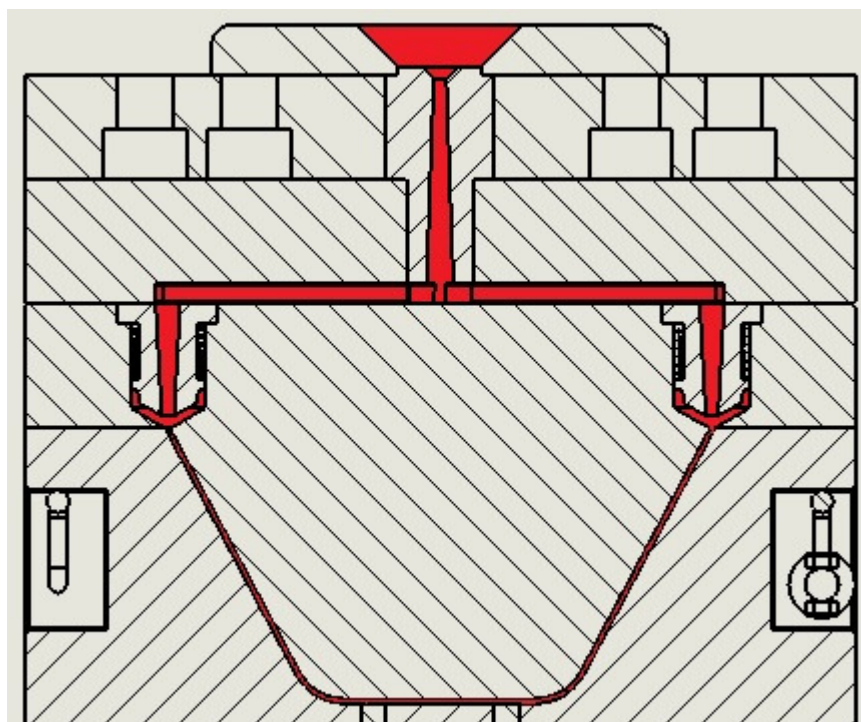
Moldes macho e fêmea desenvolvidos para a fabricação do EPR
